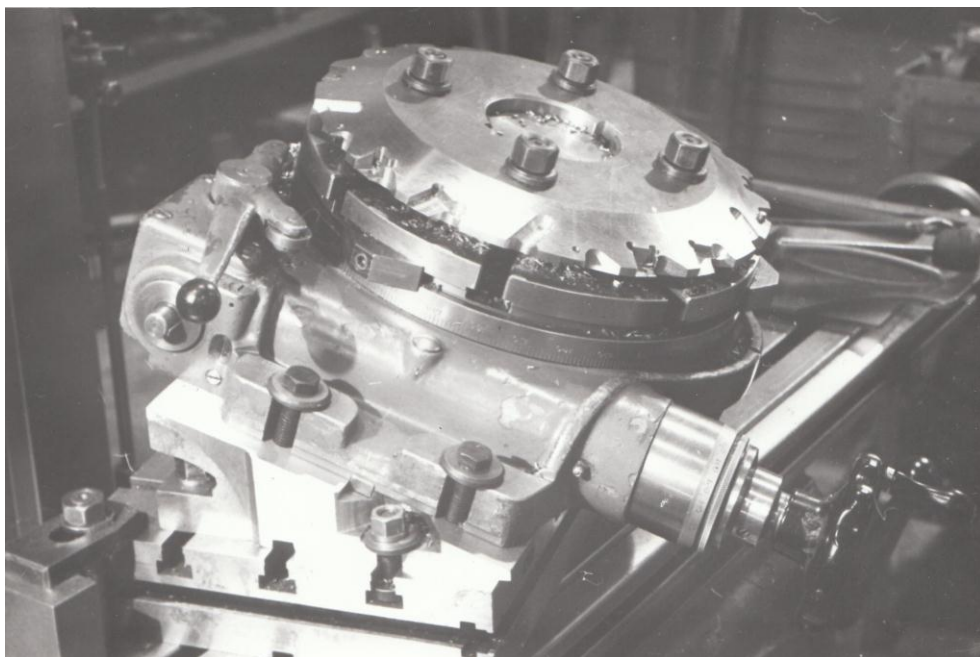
Специальное приспособление для фрезерования посадочных гнезд под пластинки
